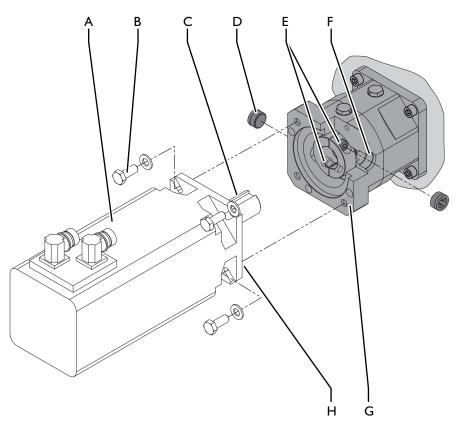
Montar el motor: Reductor planetario Güdel
